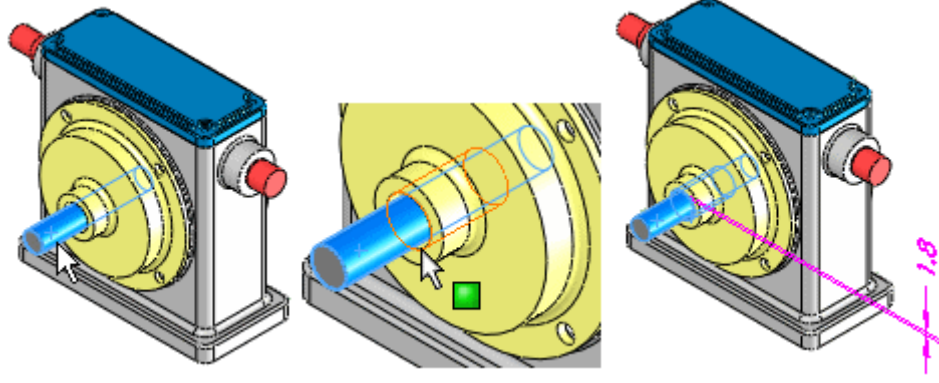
Sonsuz Dişli Şaftın geometrik toleransları
